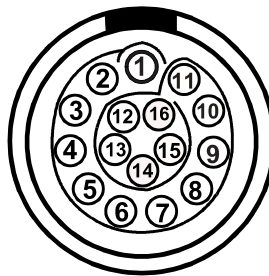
Connecteur LEMO d'interface du scanner (côté soudure)
